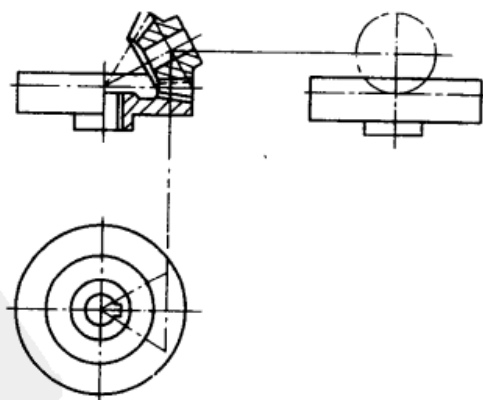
轴线成斜交的平面齿轮与锥齿轮啮合
